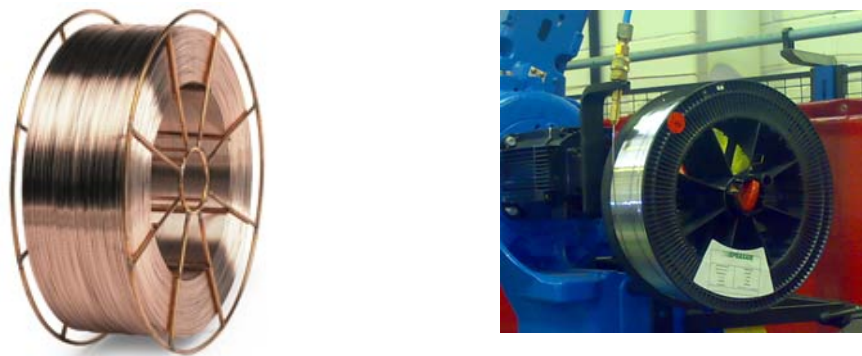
Boninas de hilo para soldadura con robot.
